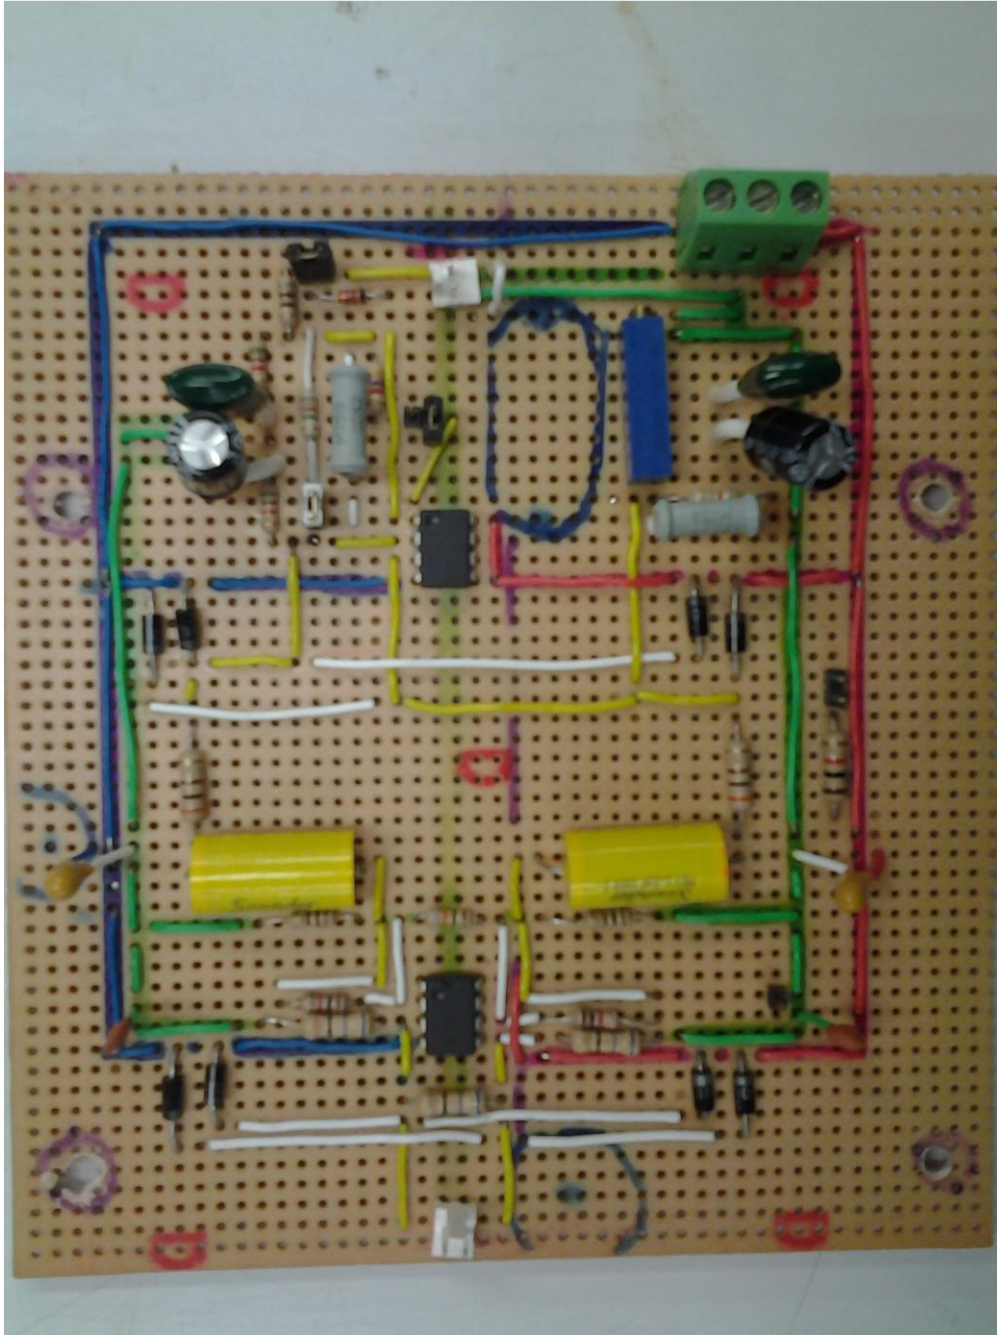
Circuito Sensor Campo-H prototipo implementado en PCB universal.
